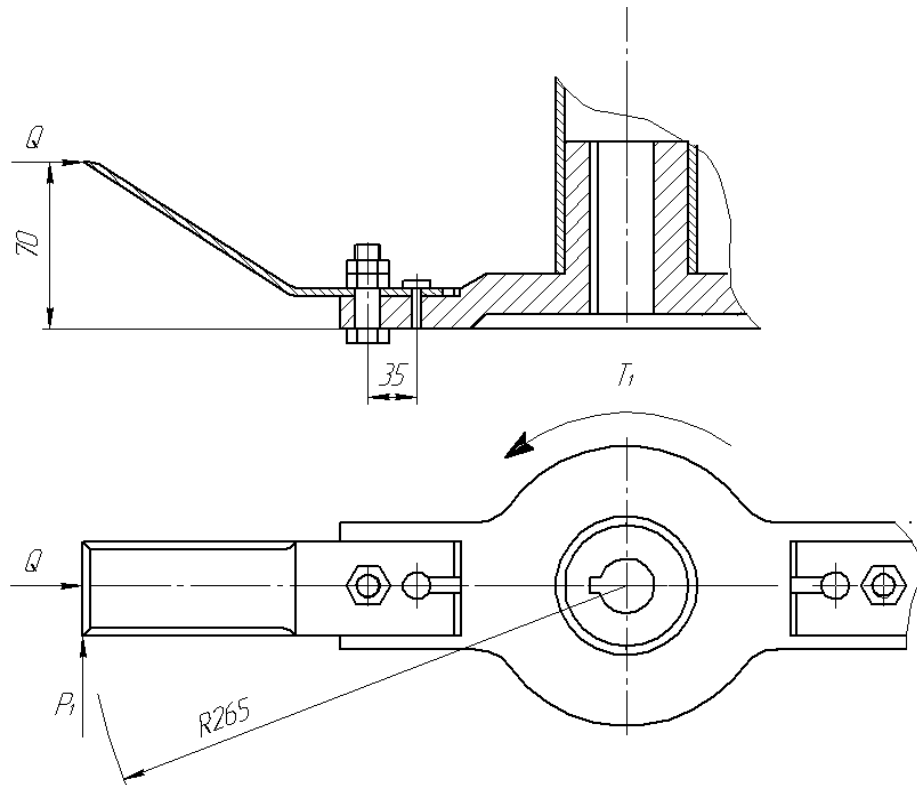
Схема навантаження болтового з'єднання шабельного ножа
